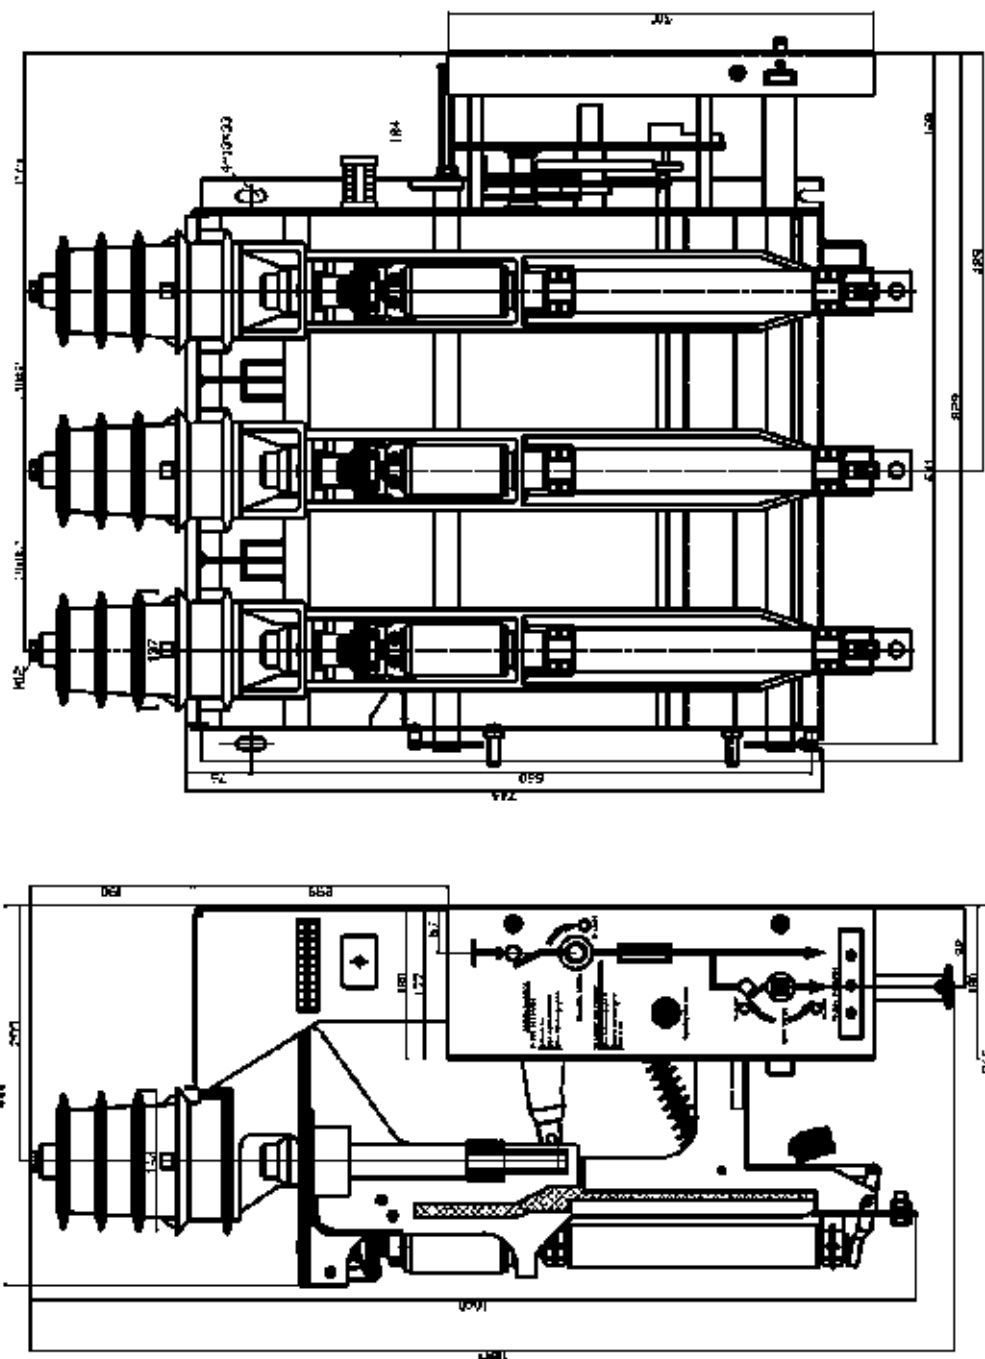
Габаритные и присоединительные размеры выключателя нагрузки FZRN
